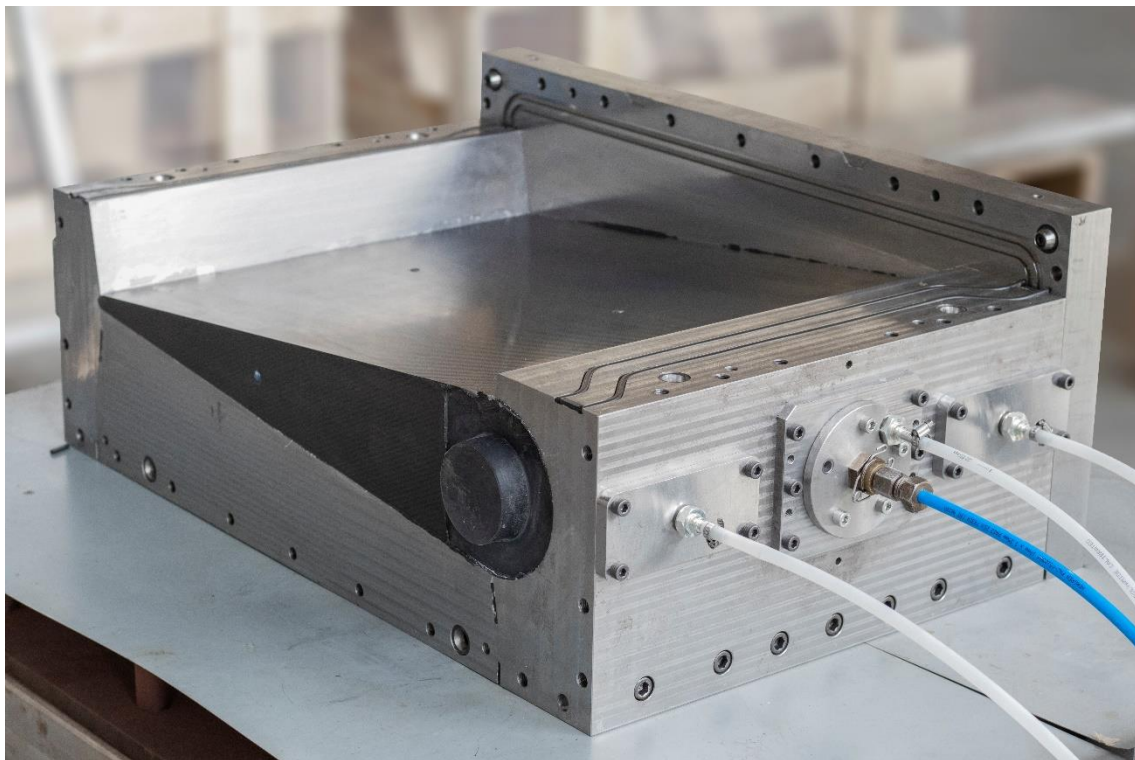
Molde produzido com o componente demonstrador de processo no interior.
